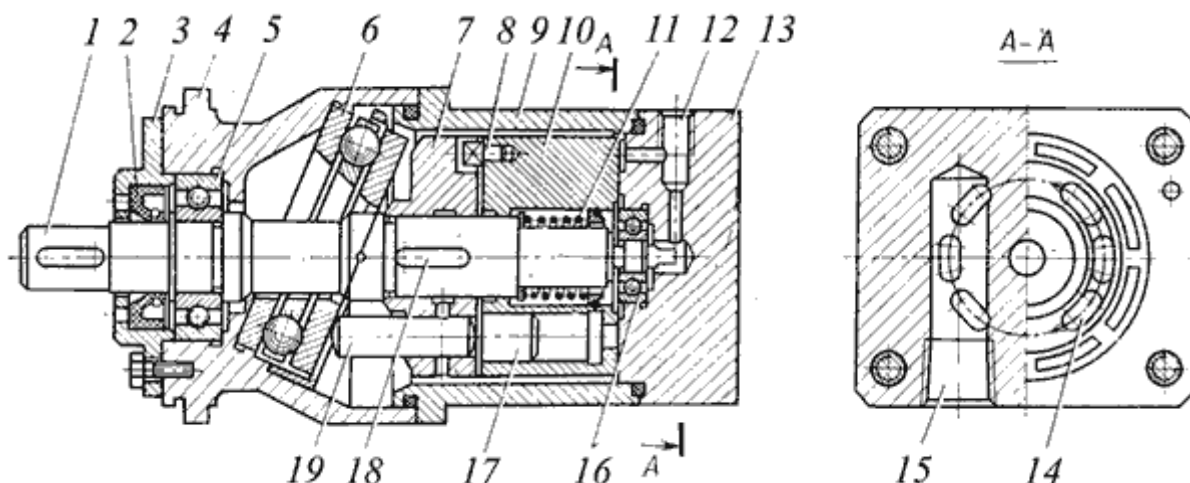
Аксиально-поршневой гидромотор типа Г15-2: 1 - вал; 2 - манжета; 3 - крышка; 4, 9 - корпус; 5, 16 - подшипник; 6 - радиально упорный подшипник; 7 - барабан; 8 - поводок; 10 - ротор; 11 - пружины; 12 - дренажное отверстие; 13 - распределительное устройство; 14 - полукольцевые пазы; 15 - отверстие напорное; 17 - поршни; 18 - шпонка; 19 - толкатель
